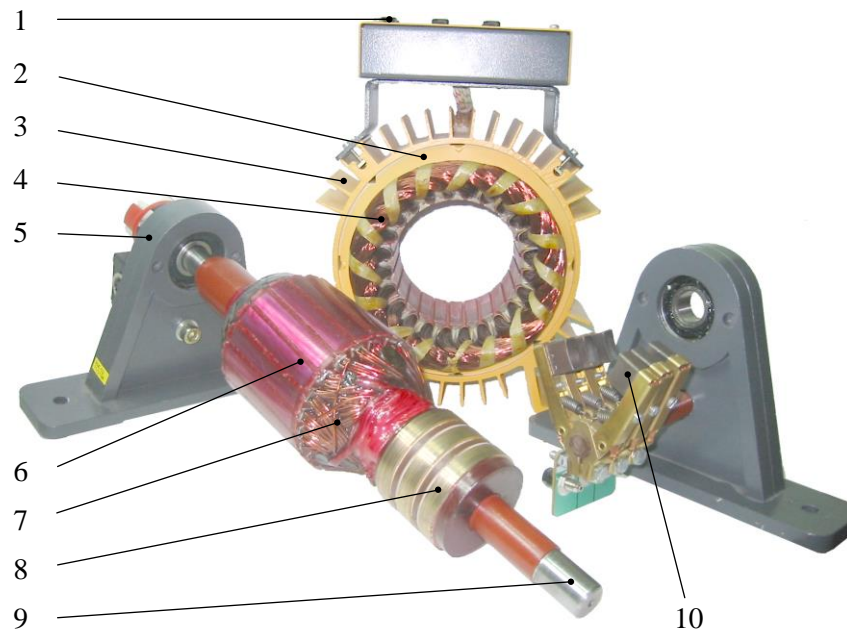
Mașină asincronă cu rotor bobinat – variantă didactică
